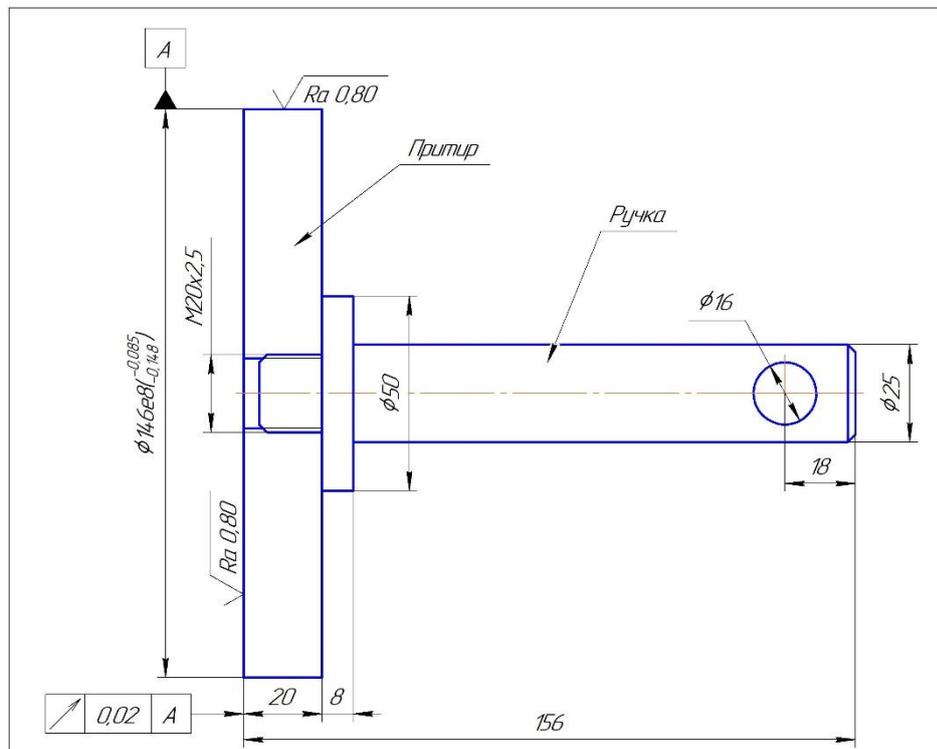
Притир для корпусу казенника А622J.304129.004.001.101
